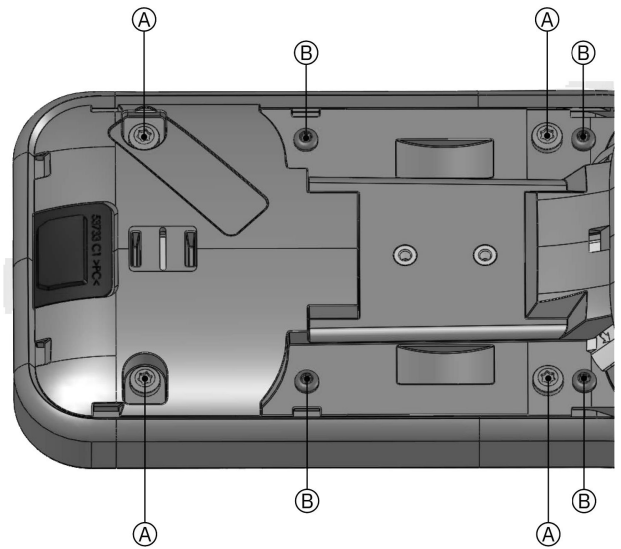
Entfernen der Schrauben A und B
